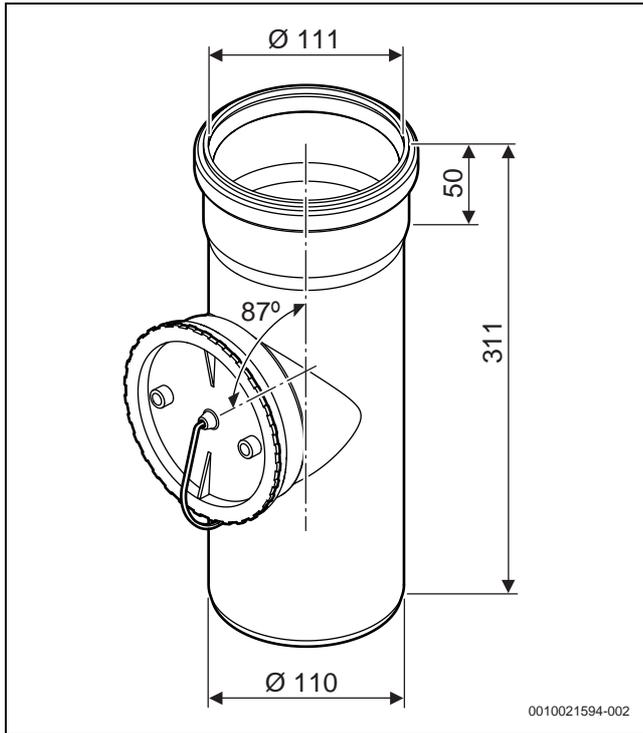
Rohr mit Prüföffnung (Maße in mm)
